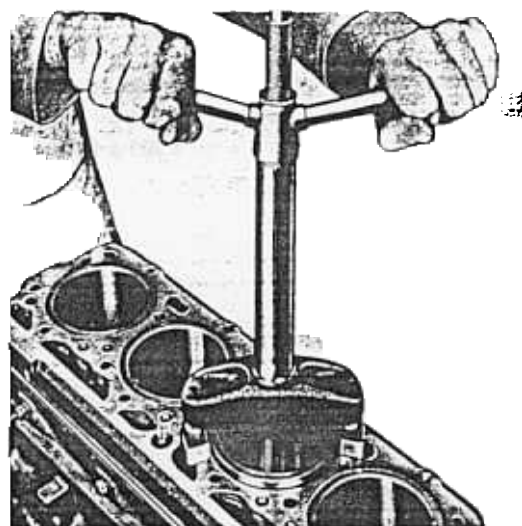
A-12M-01 — Util TF2/D-6055-A extractor de camisas de cilindro
